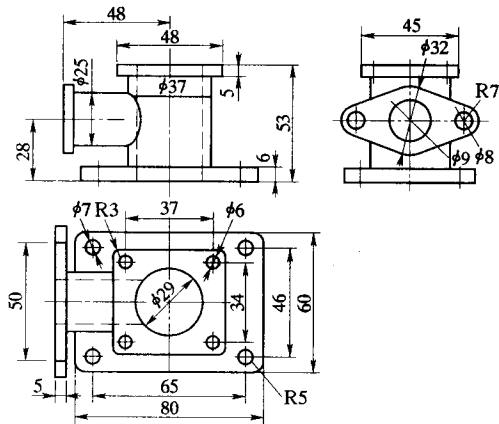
使用 AutoCAD 2004 标注的平面图形 (单位: mm)
